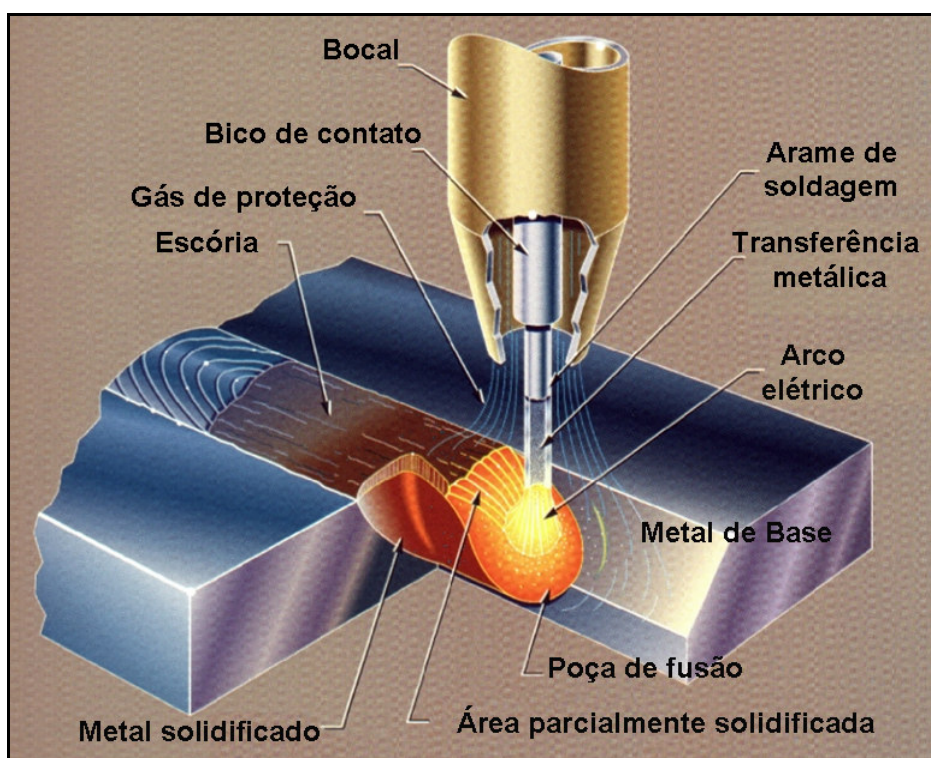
Processo de soldagem MIG/MAG (Costa, 2003).
